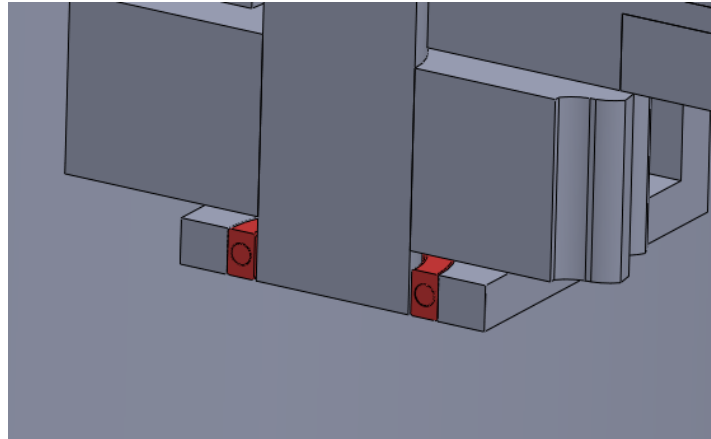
Posición del rodamiento inferior (Marcado en rojo).
